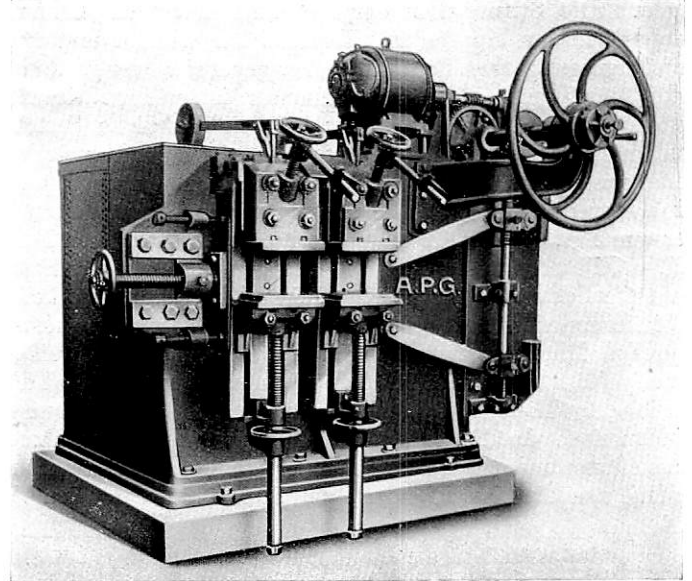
Stumpfschweißmaschine mit motorischer Stauchung für 400 kW Schweißleistung.
